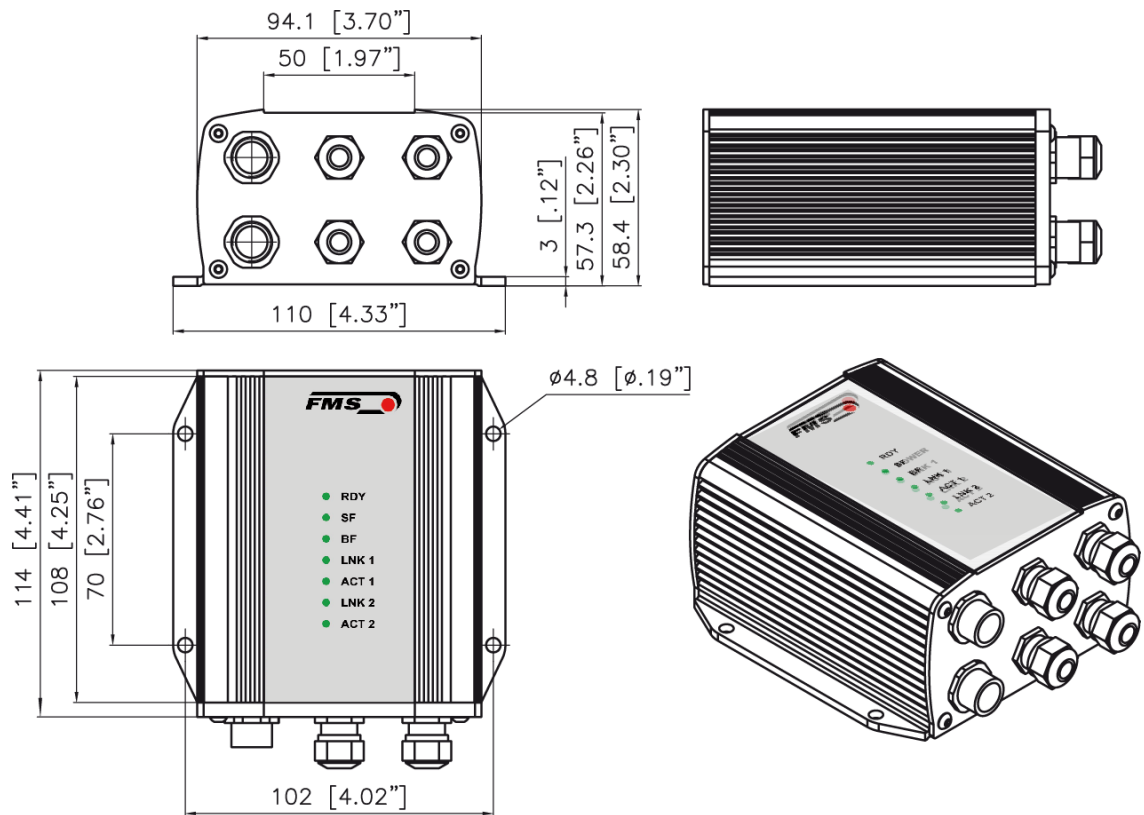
EMGZ491.W.PNET Gehäuse für Wandmontage
